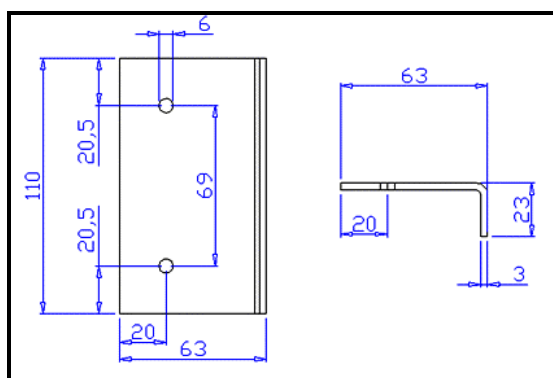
Esquema de construção da cantoneira da braçadeira do cilindro que é fixo no metalon.
